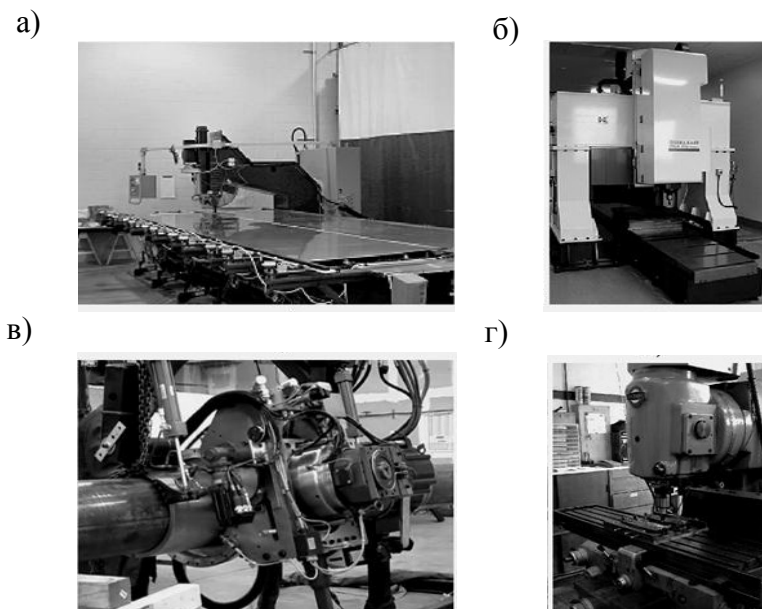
Оборудование для сварки трением с перемешиванием: а – консольного типа; б – порталного типа; в – устройство для сварки труб; г – установка на базе модернизированного фрезерного станка
